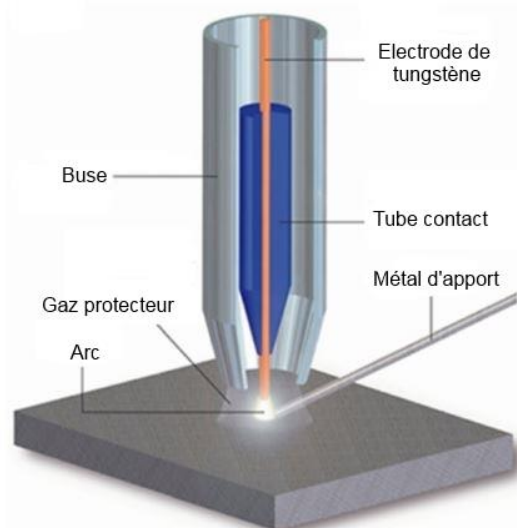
Principe de la soudure TIG ou GTAW [16]
